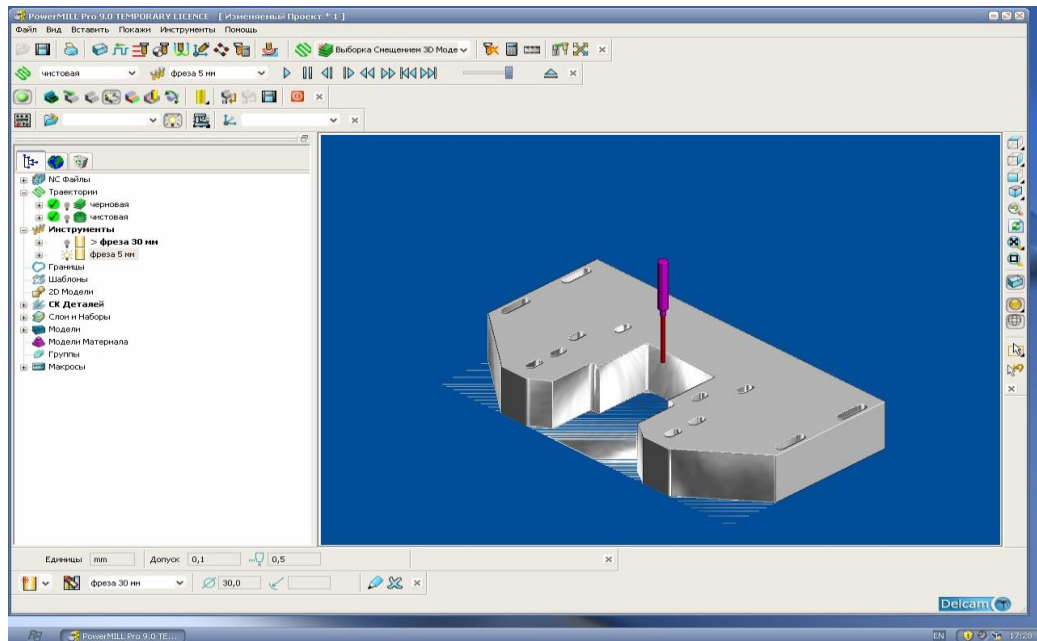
Чистова обробка «Оптимізована Z»
